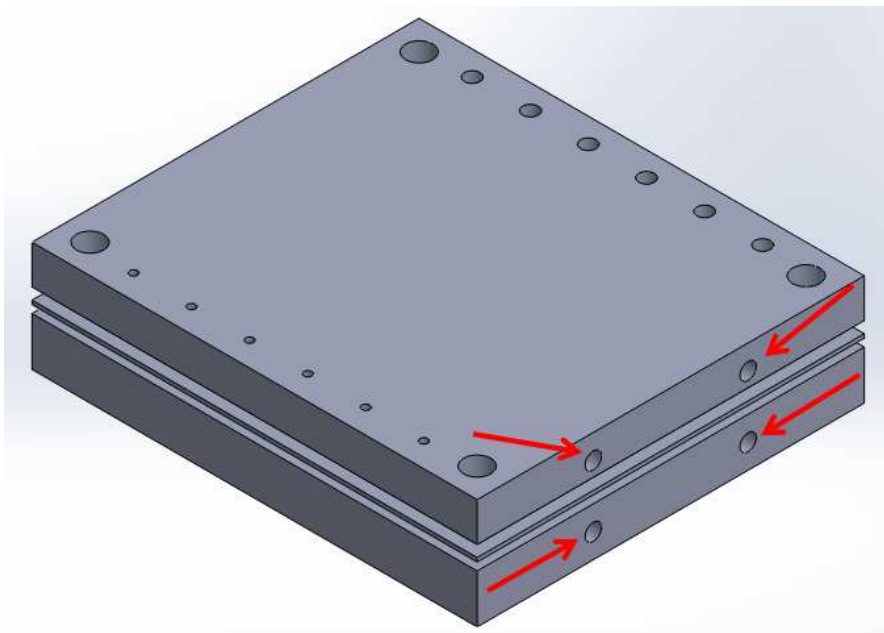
Projeto inicial para molde de cura com sistema de aquecimento incorporado.
